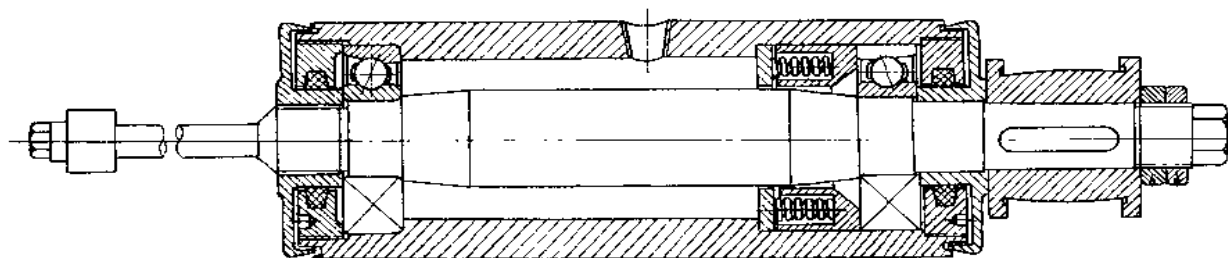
用弹簧预紧的角接触球轴承 O 型结构预调支承
